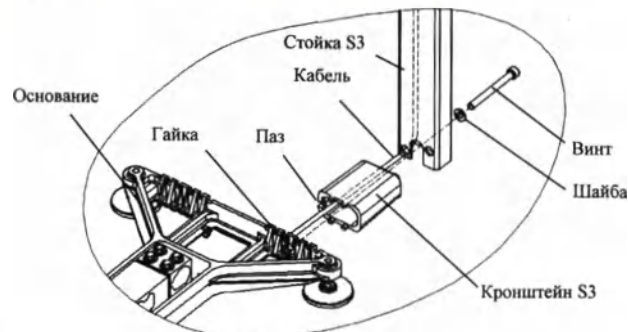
Крепление прямоугольной стойки к основанию платформы весовой
